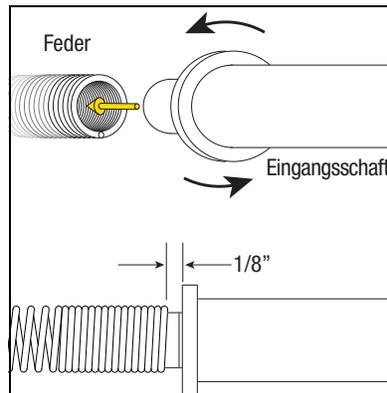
Eindrehen des Eingangsschafts entgegen dem Uhrzeigersinn in die Encoder-Feder
